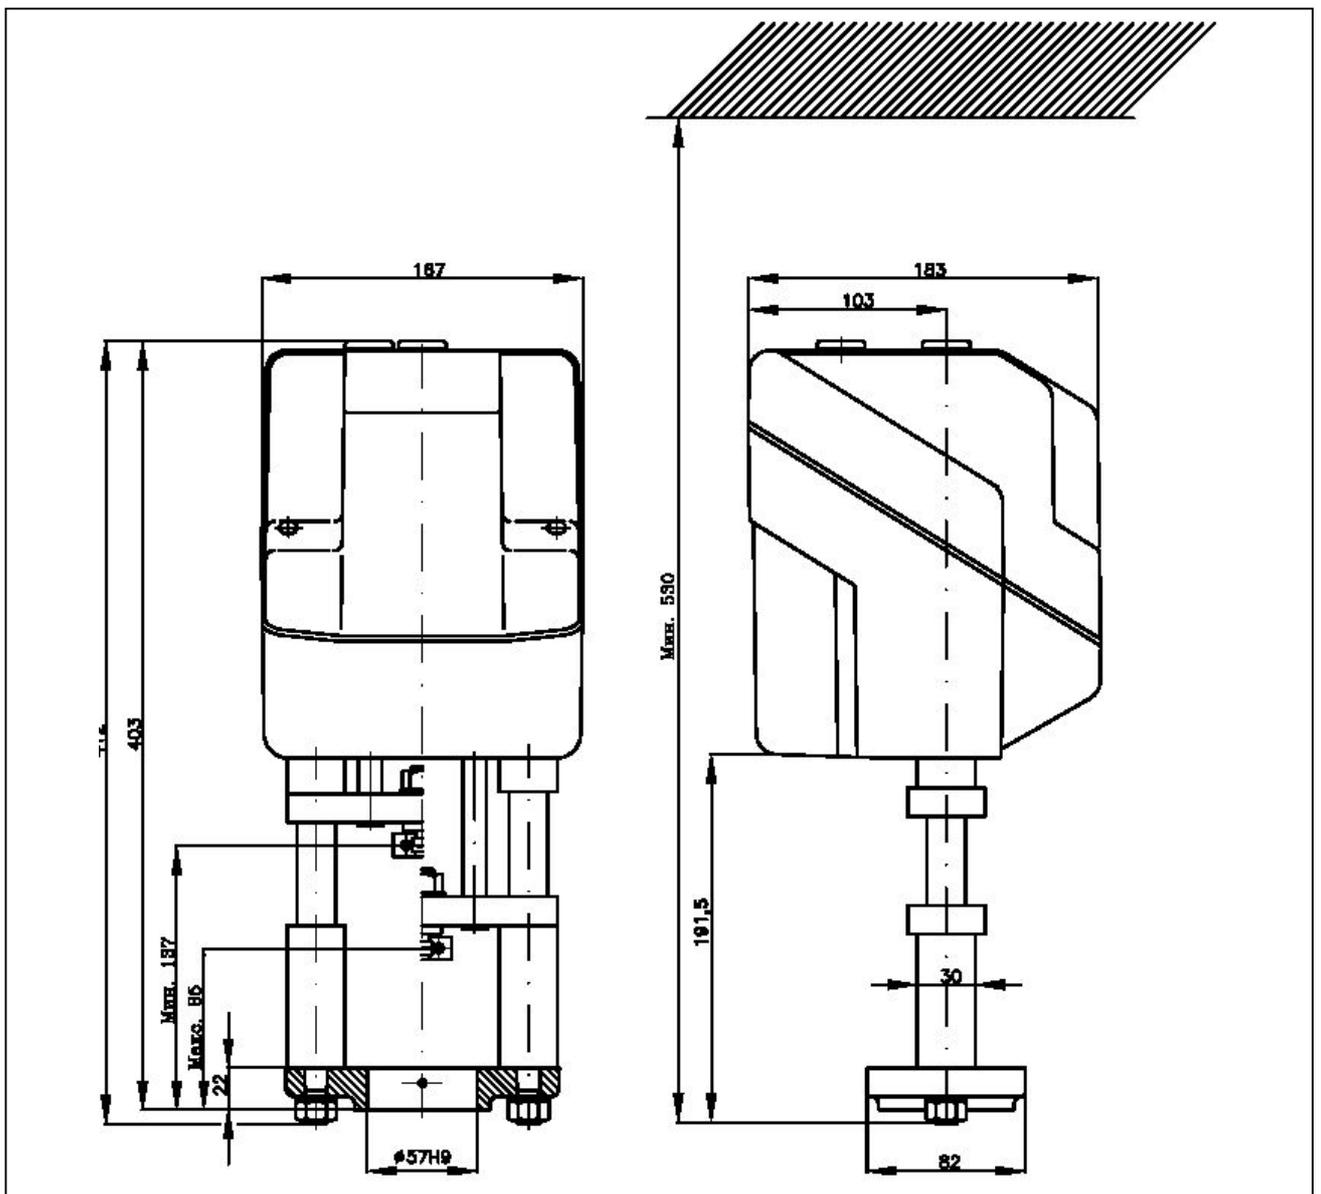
Габаритные и присоединительные размеры AMV 550.
